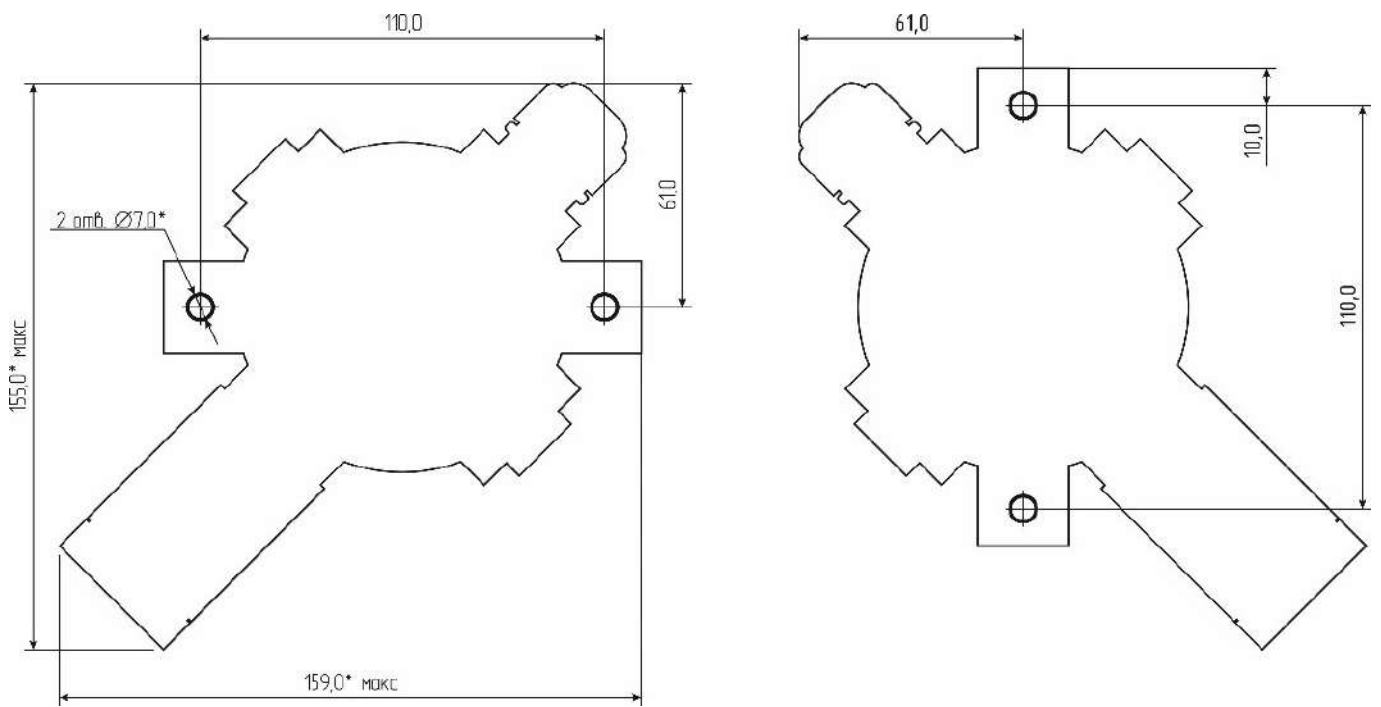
Разметка отверстий для крепления БСУ-КЕ
